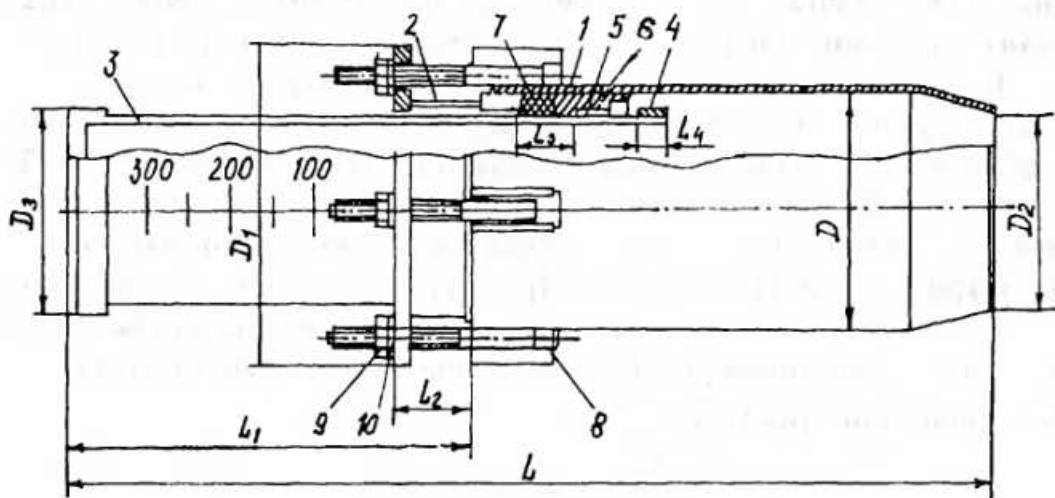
Одинарний сальниковий компенсатор: 1 - корпус; 2 - ґрунд-букса; 3 - патрубок; 4 - запобіжне кільце; 5 - контр-букса; 6 - шнур-набивка; 7 - ущільнювальне кільце; 8 - болт; 9 - гайка; 10 - шайба
